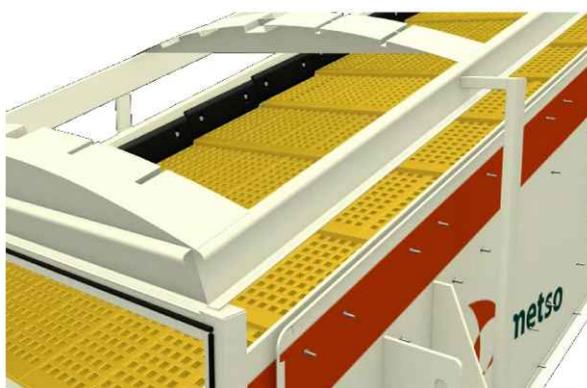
Beispiel einer Dachkonstruktion mit Dachbögen
